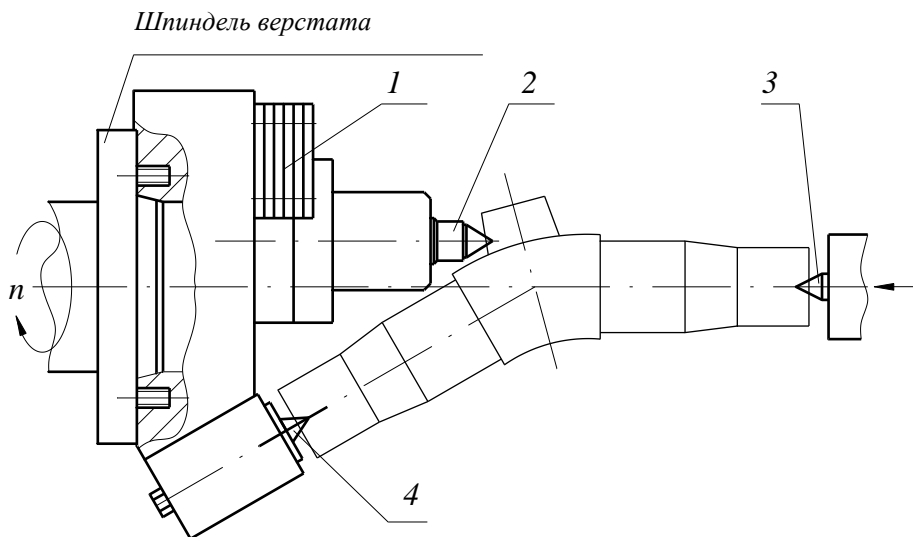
Базування і затиск криволінійної вісі у пристрої металорізального верстата.
